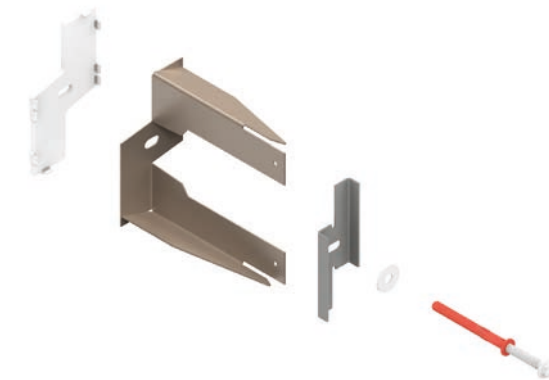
Wandabstandshalter (Explosionszeichnung)
